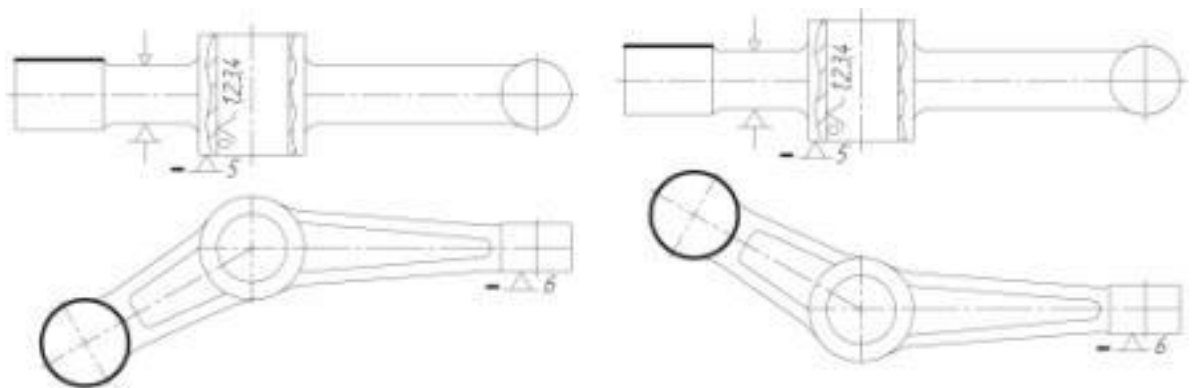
Схема базування заготовки на вертикально-свердлильній 10 та координатно-розточувальній 15 операціях
